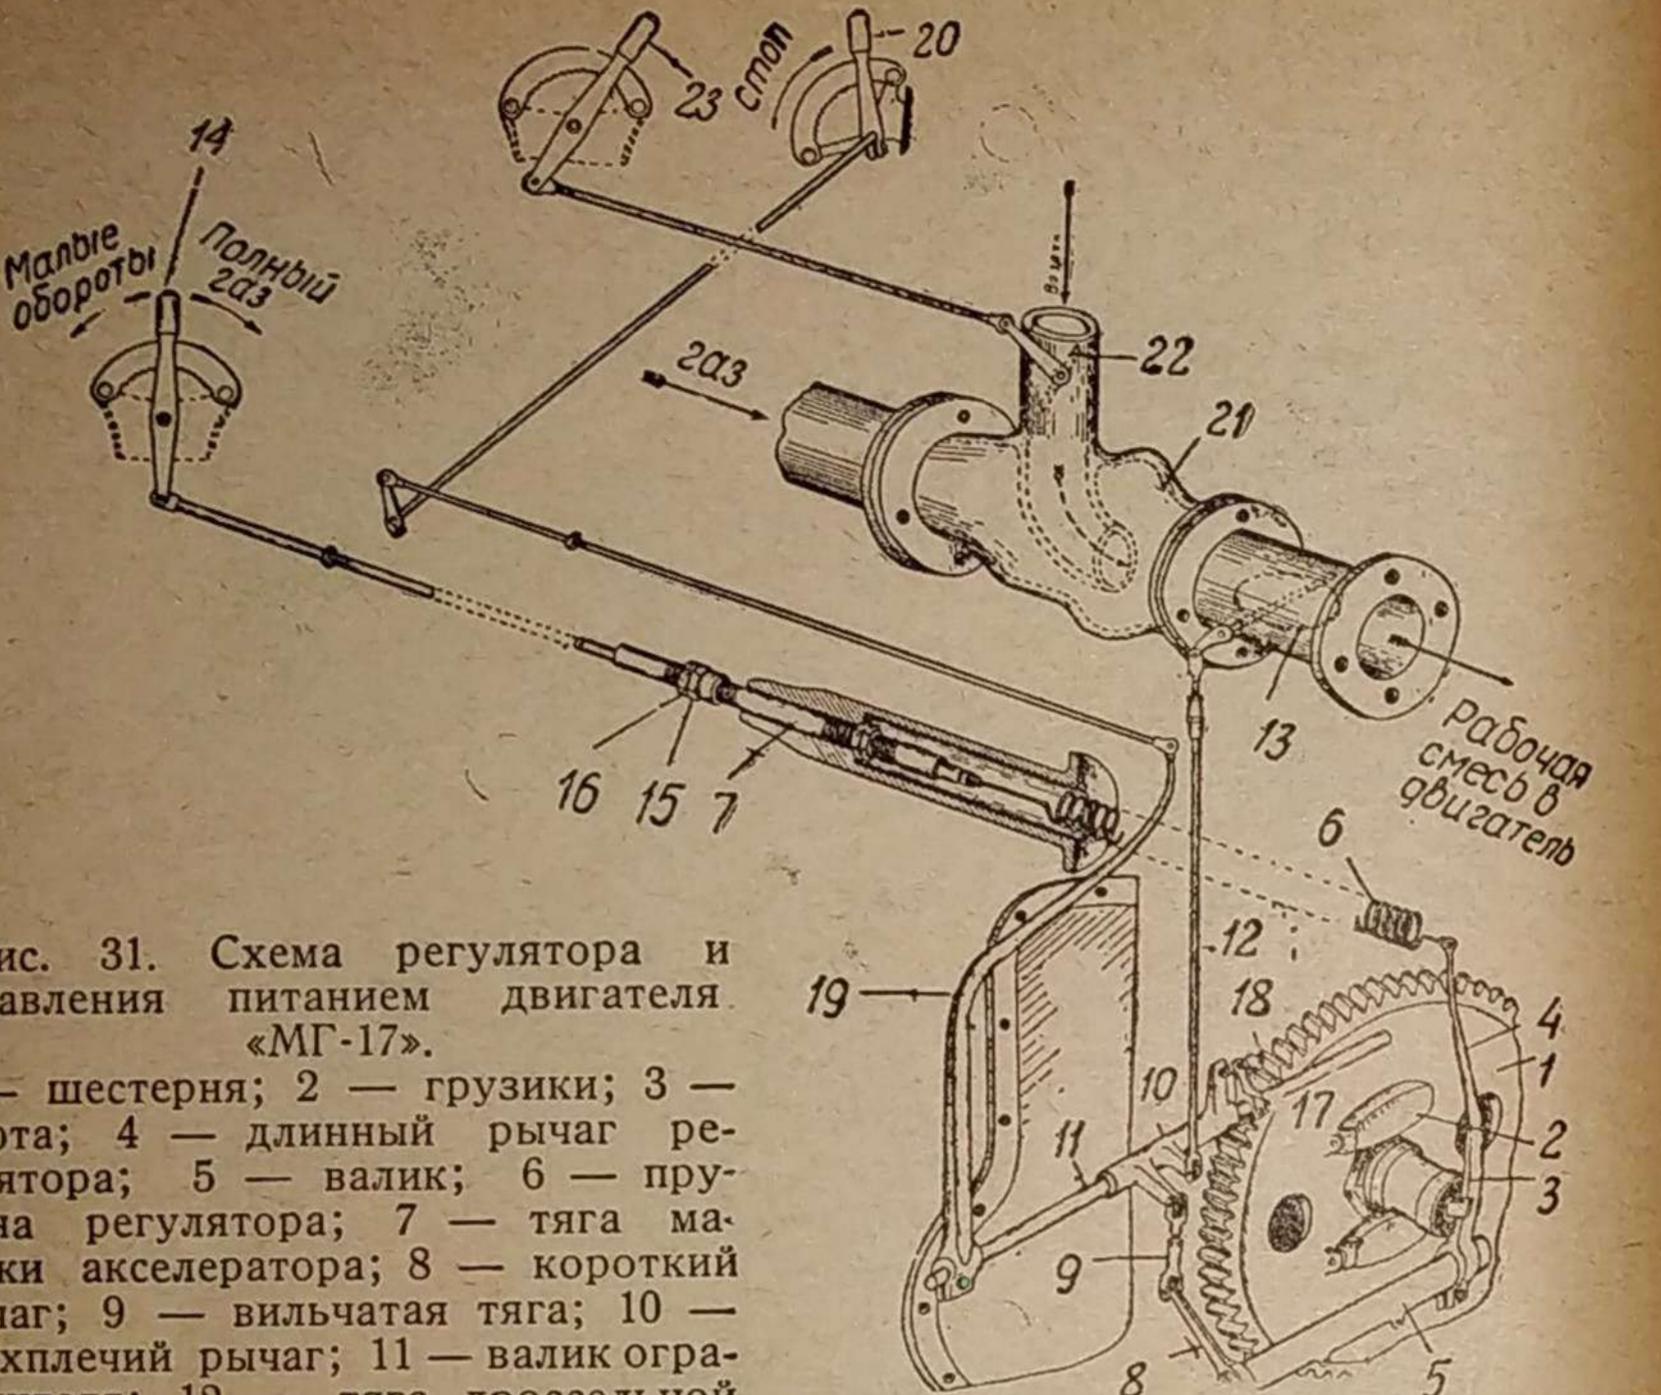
Схема регулятора и управления питанием двигателя «МГ-17».
